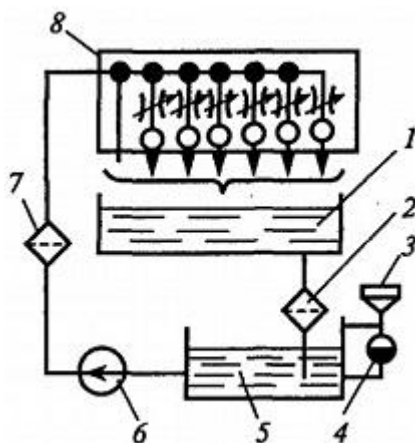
Схема циркуляционного смазывания с принудительной циркуляцией масла под давлением: 1 — коробка; 2 — сливной фильтр; 3 — заправочное отверстие; 4 — маслоуказатель; 5 — резервуар; 6 — насос; 7 — фильтр тонкой очистки; 8 — распределитель
